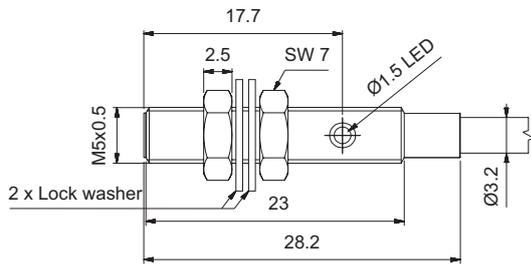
Kurze Ausführung, bündiger Einbau, Kabel
